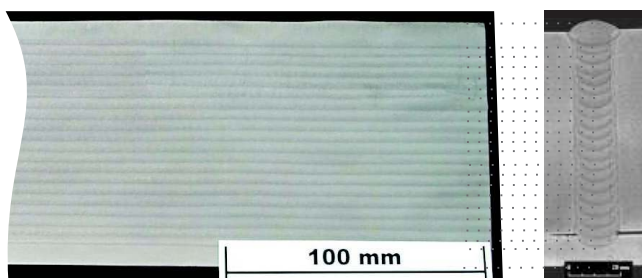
Nahtaufbau beim Engspaltschweißen mit Lichtbogensensor
